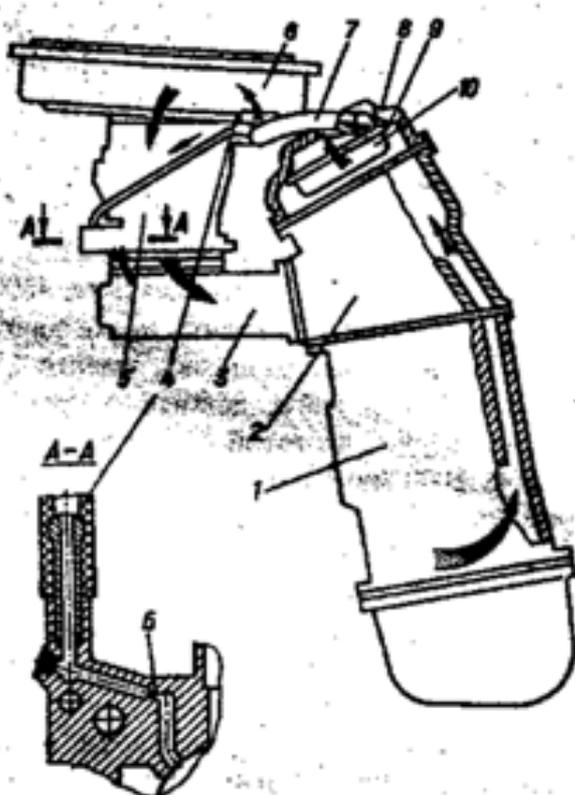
Схема системы вентиляции картерных газов: 1 - блок цилиндров; 2 - головка цилиндров; 3 - впускной коллектор; 4 - трубка отсоса картерных газов в карбюратор; 5 - карбюратор; 6 - воздушный фильтр; 7 - шланг вентиляции картера; 8 - прокладка; 9 - крышка головки цилиндров; 10 - маслоотражатель; Б - калиброванное отверстие диаметром 1,5 мм
